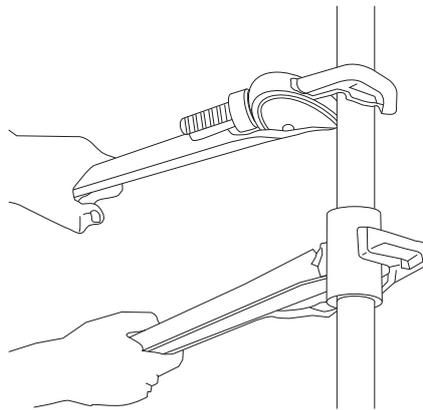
Posicionamiento correcto de las llaves en el conjunto de ejes
